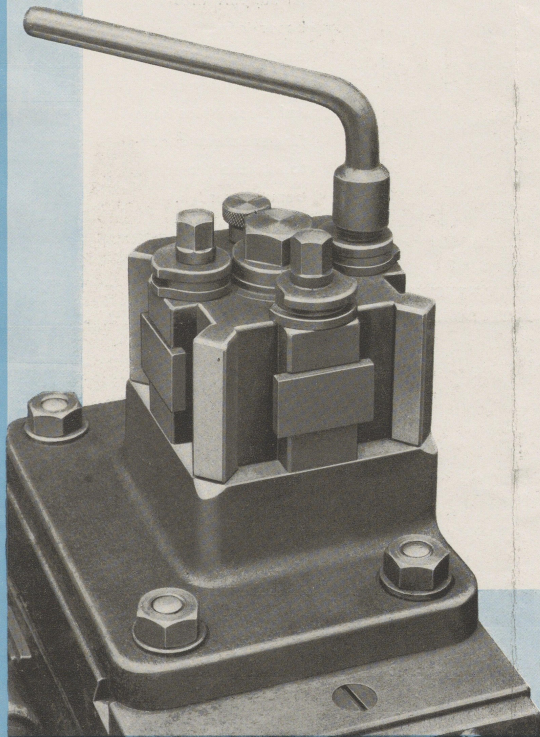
Schnellwechselstahlhalter mit Werkzeughaltern. Vorn Werkzeughalter mit Auslösevorrichtung für Spiralbohrer.
